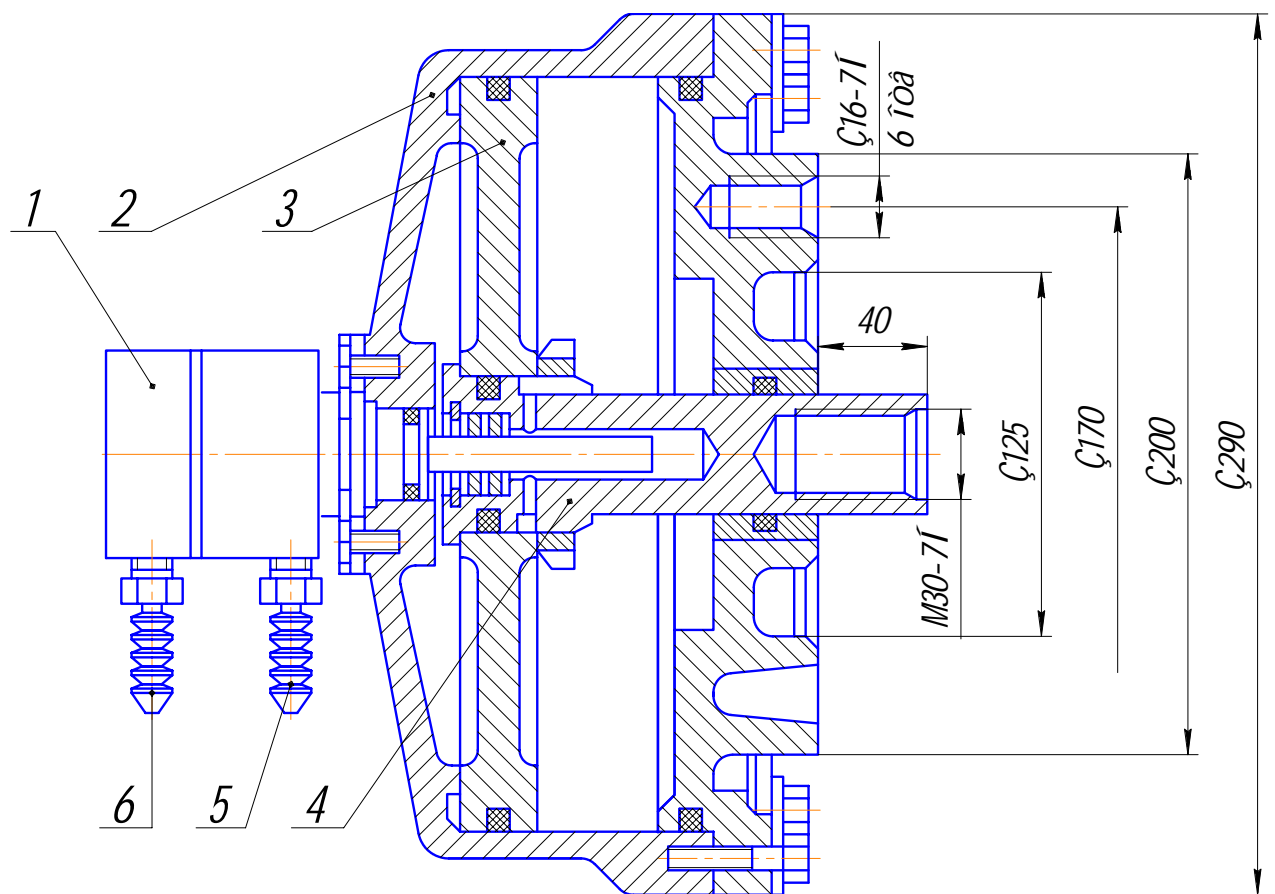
Пневматичний механізований привод моделі П-ЦВ-260:
